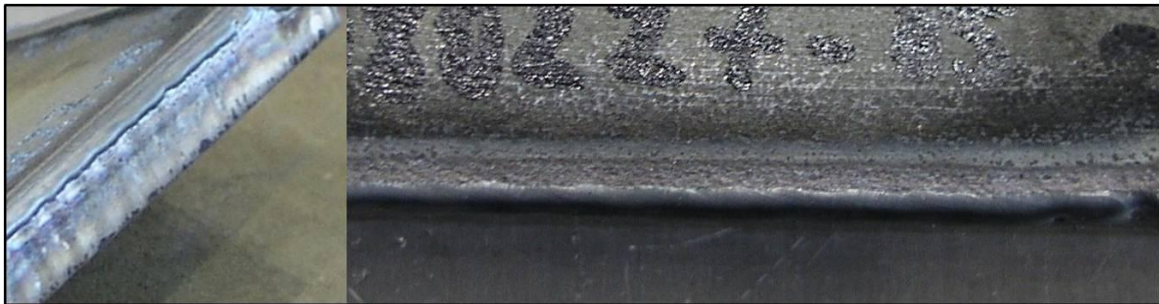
Schweißnaht der Oberkante bei einem Brennerwinkel α von 45°
